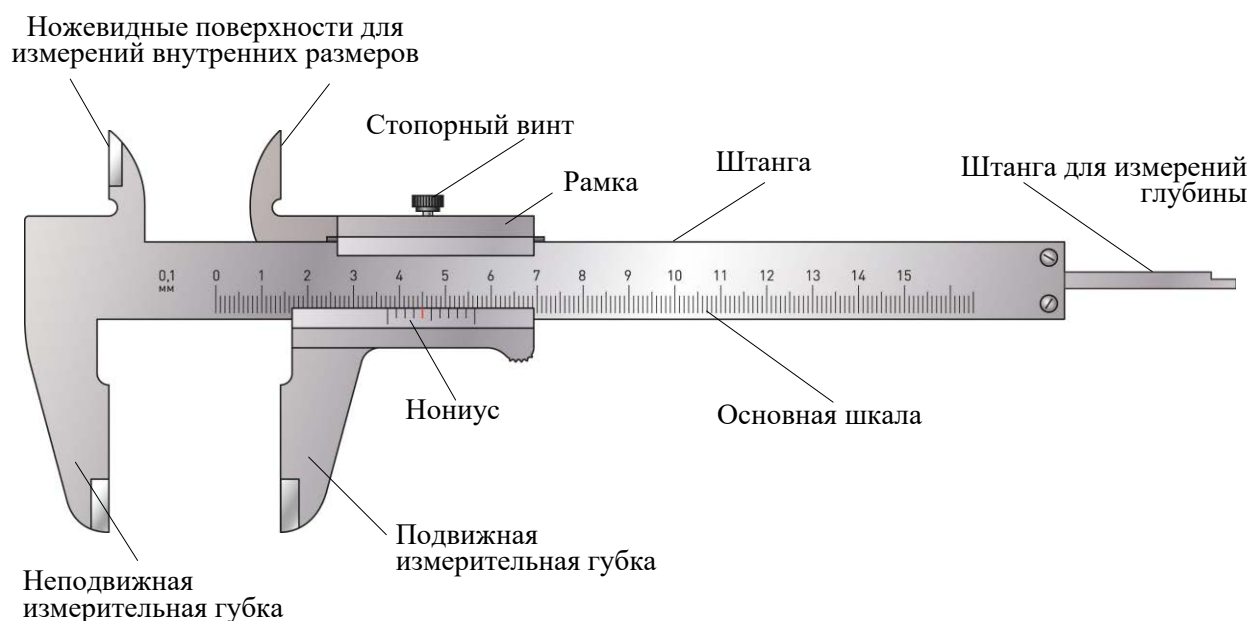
Внешний вид штангенциркуля ШЦ
